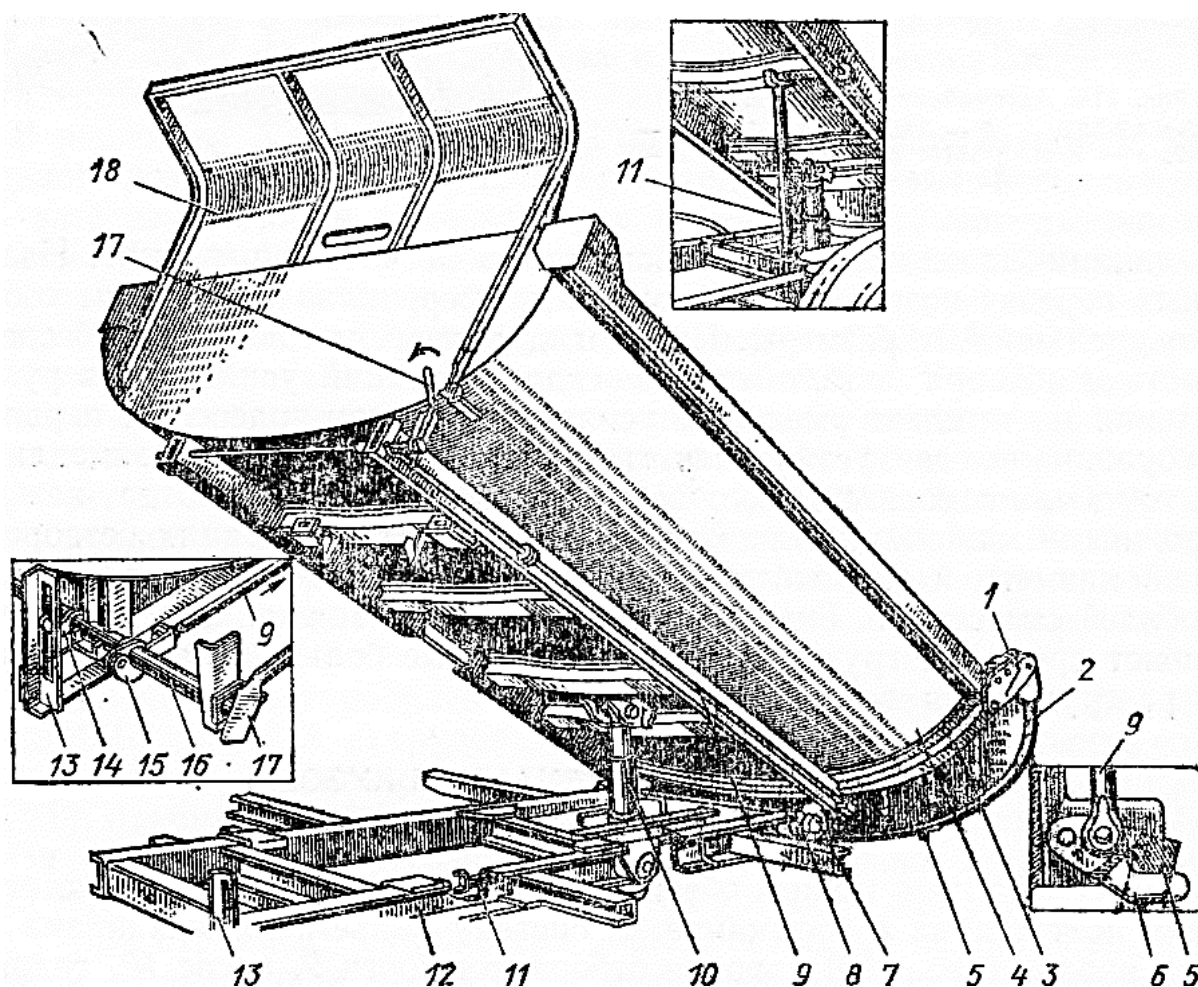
Цельнометаллический кузов автомобиля-самосвала ЗИЛ-ММЗ-555: 1 – кронштейн подвески заднего борта; 2 – задний борт; 3 – поперечная балка; 4 – плат-форма; 5 – цапфа запорного крюка; 6 – запорный крюк; 7 – ось опрокидывания плат-формы; 8 – кронштейн оси опрокидывания; 9 – тяга; 10 – подъемник; 11 – упорная штанга; 12 – надрамник; 13 – кронштейн для автоматического открывания заднего борта; 14 – рычаг автоматического открывания заднего борта; 15 – скоба; 16 – вал управления -шторами заднего борта; 17 – рукоятка; 18 – козырек
